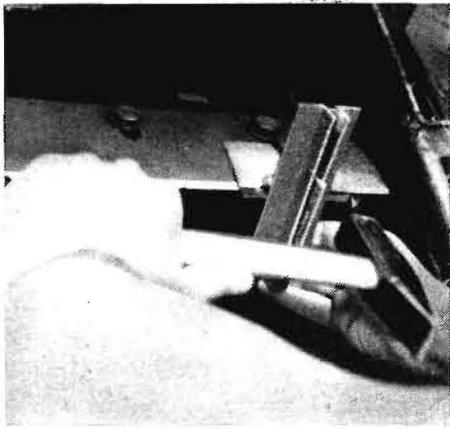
Aufnahmen des Verschleißzustands der Häckselmesser mit Hilfe eines Bleiabdrucks
